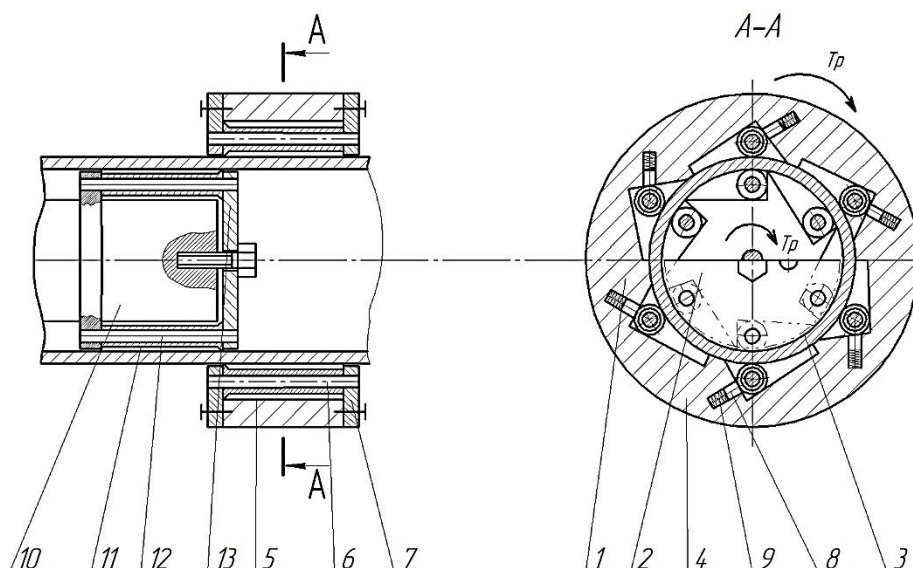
Устройство для отрезки трубчатых заготовок от цилиндрической трубы
